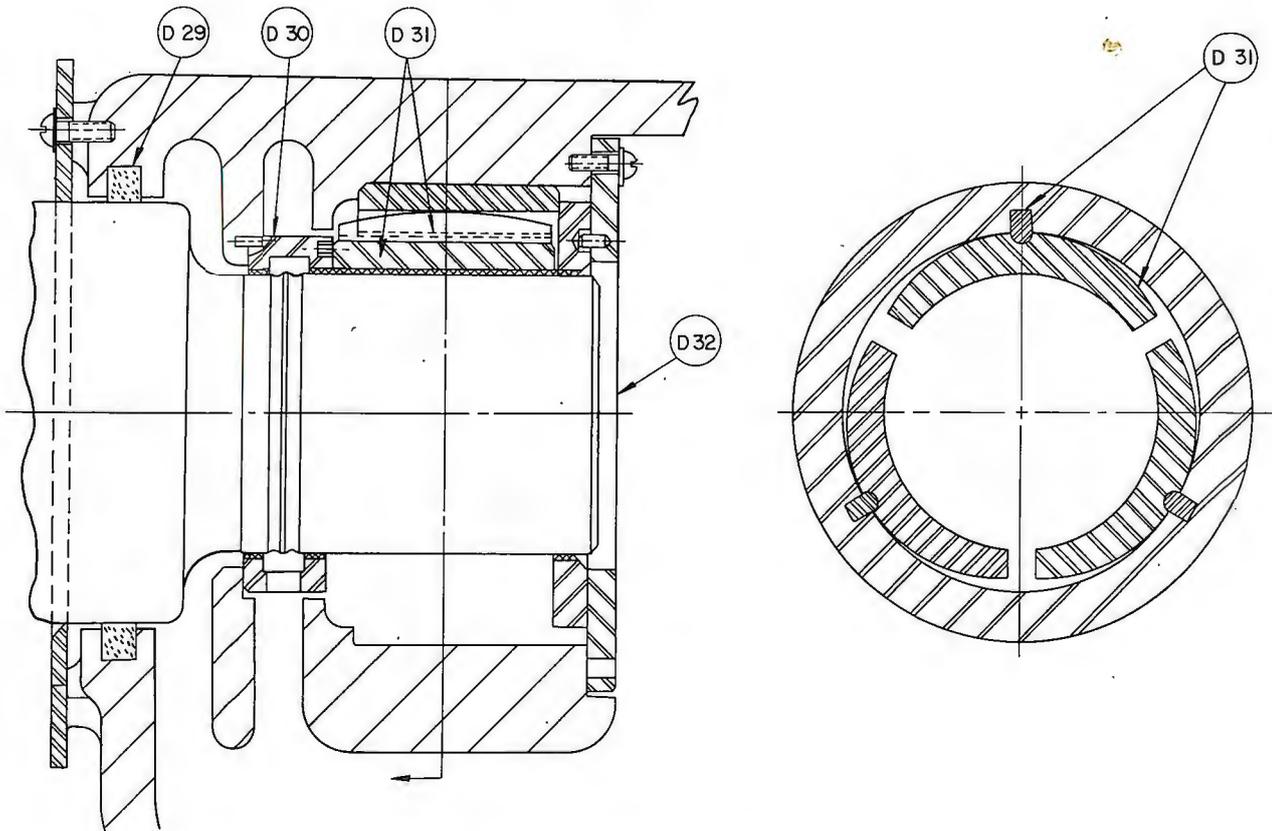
Motorendlager (Maschine - Typen 3 bis 7)
